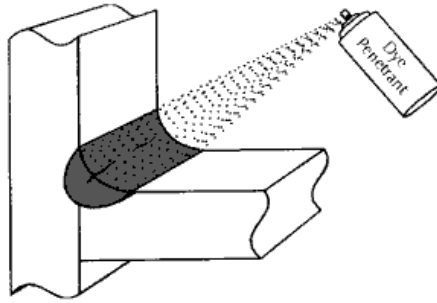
Aplicación de líquido penetrante en unión soldada.
